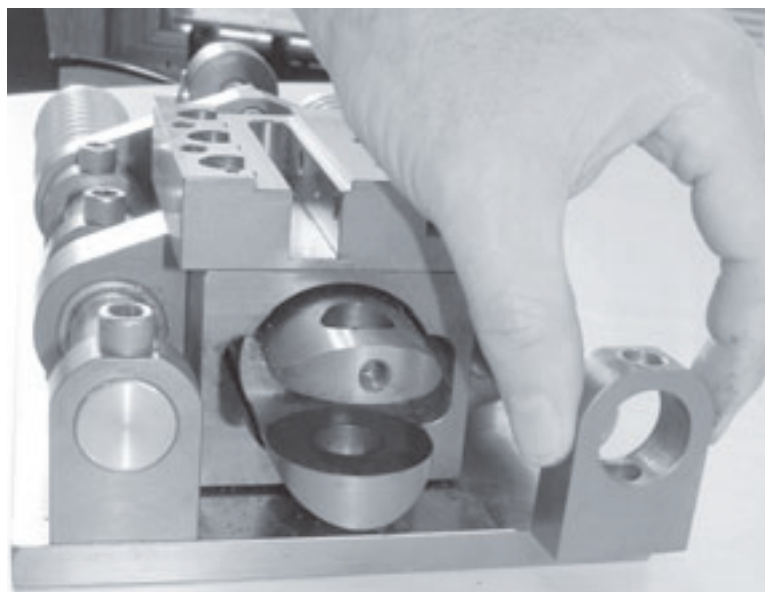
Демонтируйте опоры вала для возможности снятия подающего блока и подающего винта в сборе.
